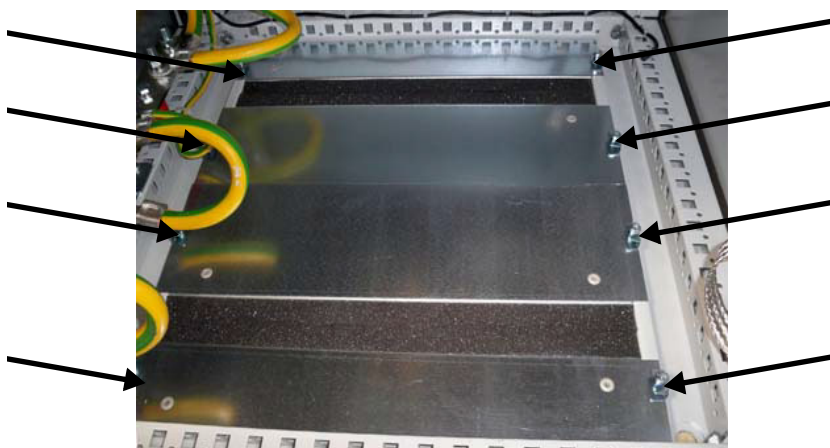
Rimozione delle piastre sul fondo dell'armadio CC
